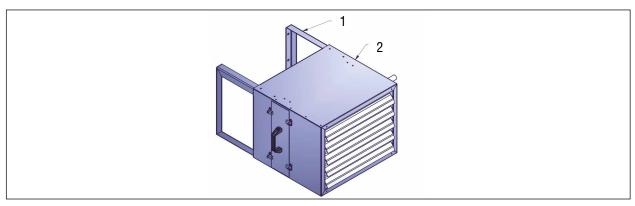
Montage mural d'un réchauffeur d'air (LH)
